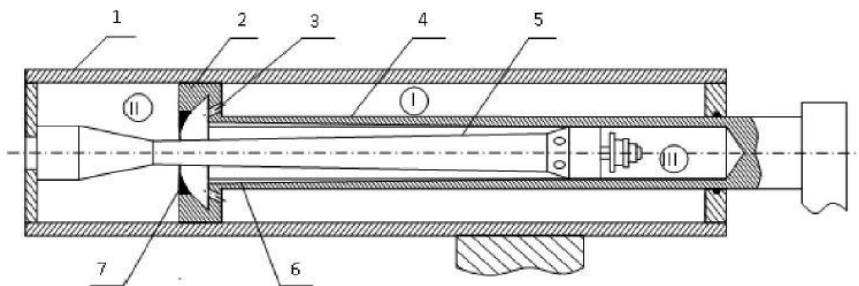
Схема тормоза отката: 1. Цилиндр тормоза отката; 2. Поршень; 3. Отверстие для слива масла; 4. Шток поршня; 5. Регулирующий шток; 6. Трещина; 7. Регулирующее кольцо
